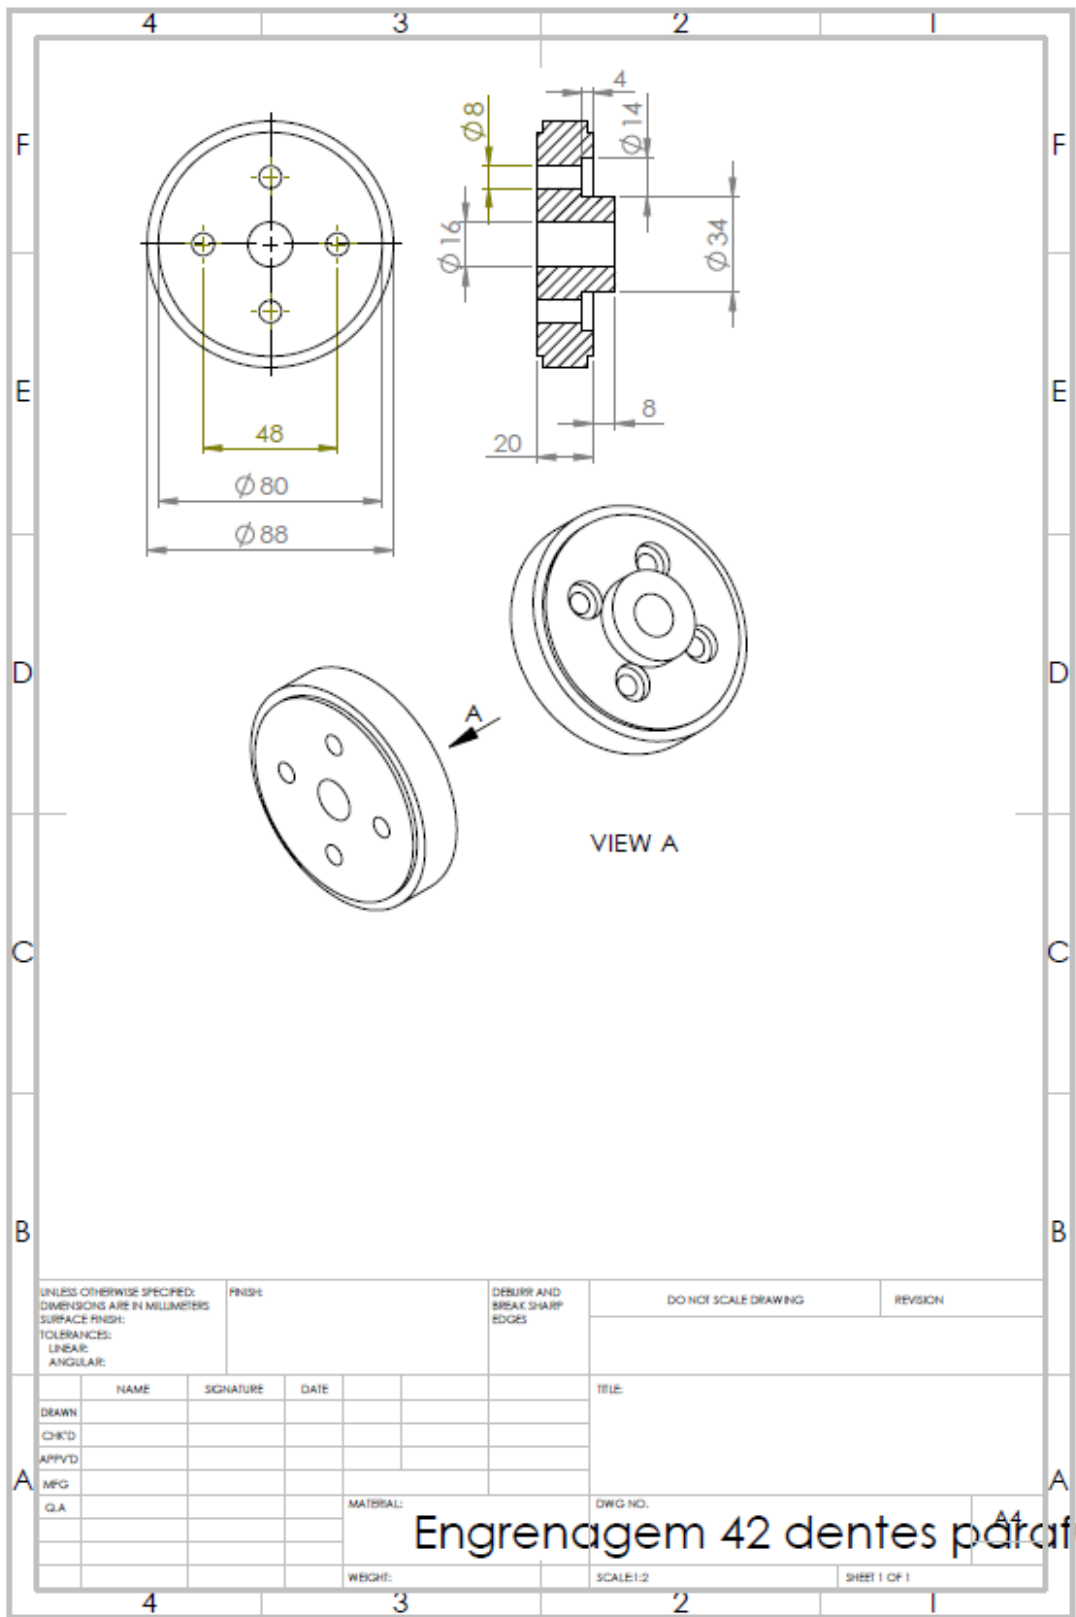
C, Desenho para engrenagem de 42 dentes com perfurações para acoplamento de uma junta universal [Foto do autor].
